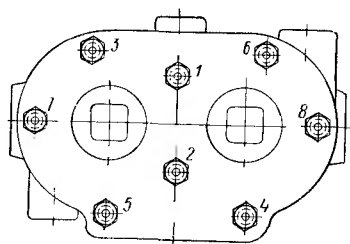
Порядок затяжки гаек крепления головки цилиндров компрессора
